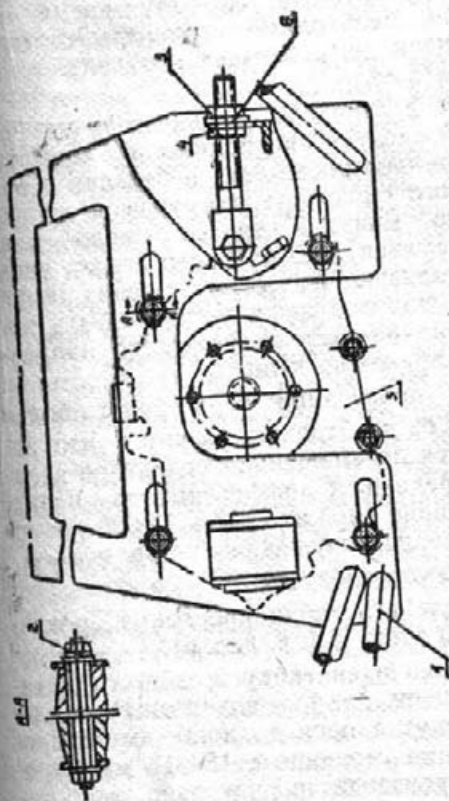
Схема натяжения цепной передачи с двигателя на редуктор:
